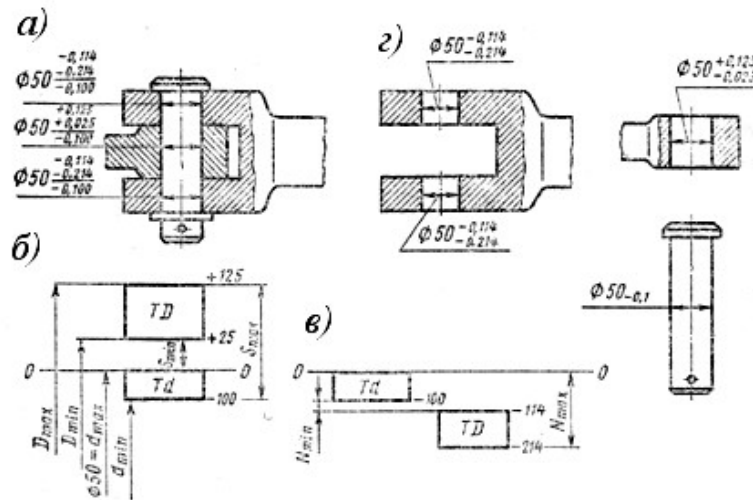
Приклади креслень деталей, складального креслення та схем полів допусків
